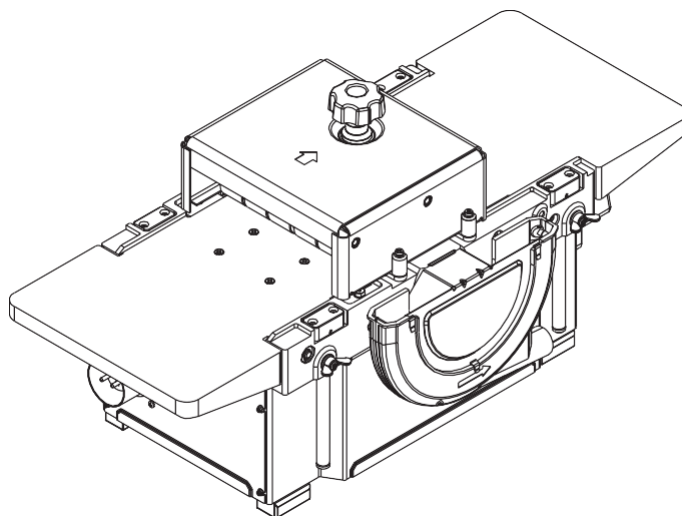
Станок строгальный с приспособлением прижимным 0000-03 (0000-03-x1).
